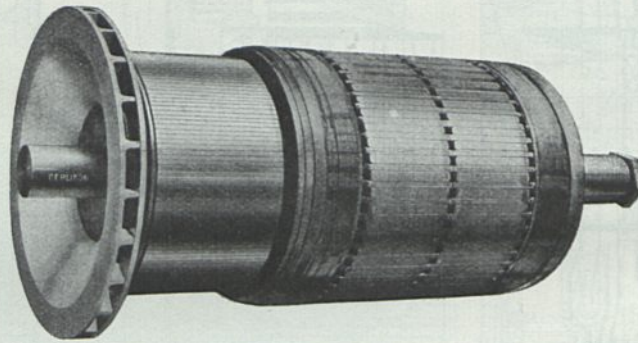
Untergestell-Motoranker mit angebautem Schleuderrad (M.F.O.).
